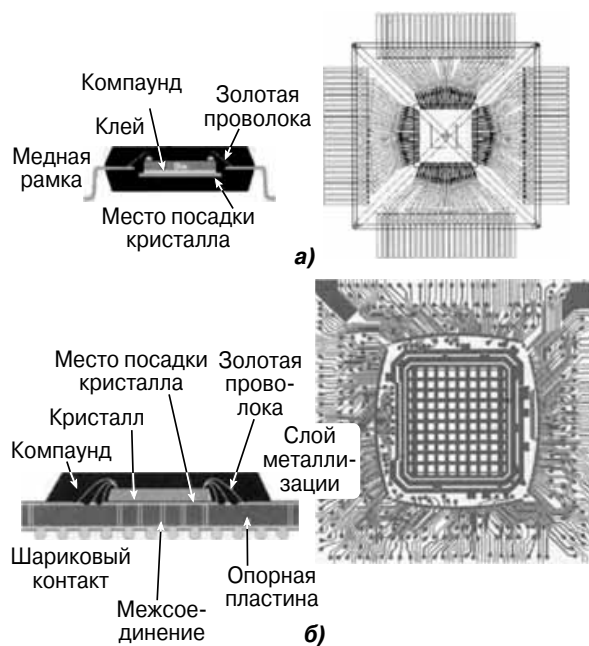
Вид сверху и изображение в поперечном разрезе корпусов с выводной рамкой (а) и типа BGA (б).
